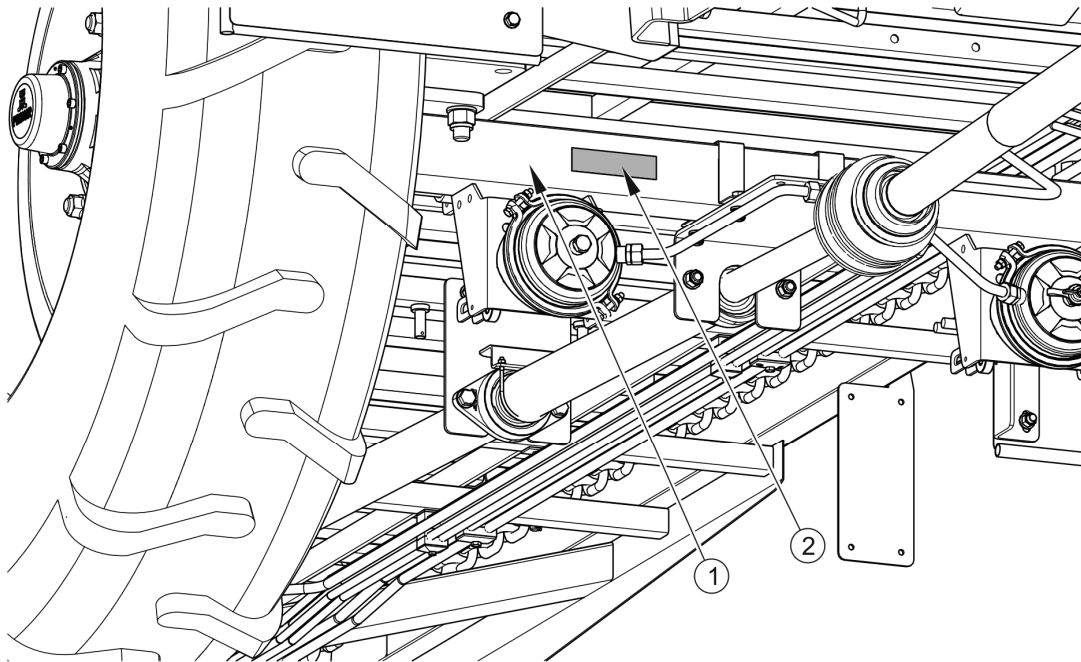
Emplacement de la plaque signalétique de l'essieu moteur
